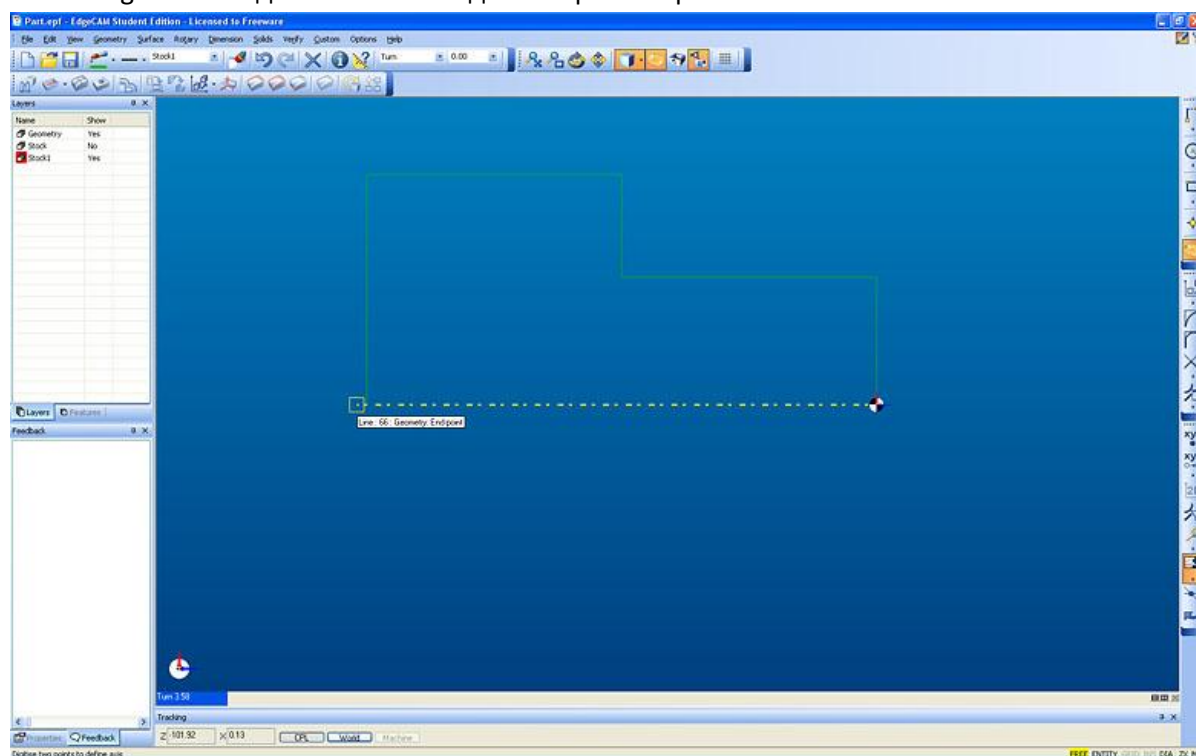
Edgcam. Создание заготовки для токарной обработки
